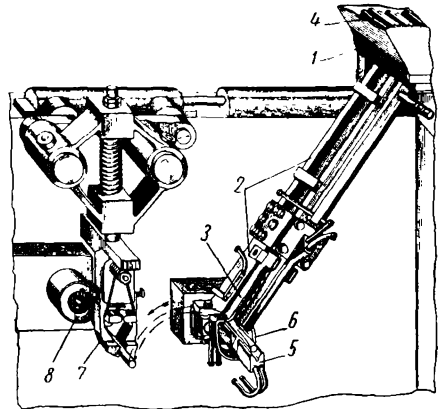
Схема агрегата для автоматического нагрева и высадки мерных заготовок
